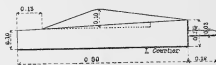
Mandrin en deux pièces pour moulage de condenseurs.
